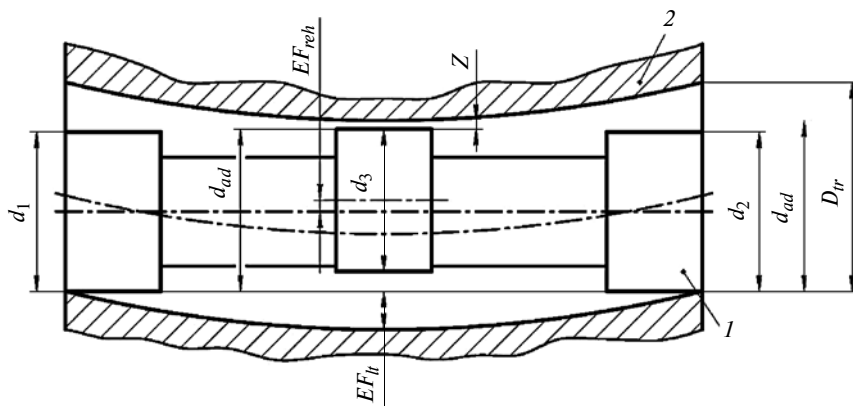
Схема положения сборного корпуса 1 ракетного двигателя в пусковой трубе 2
